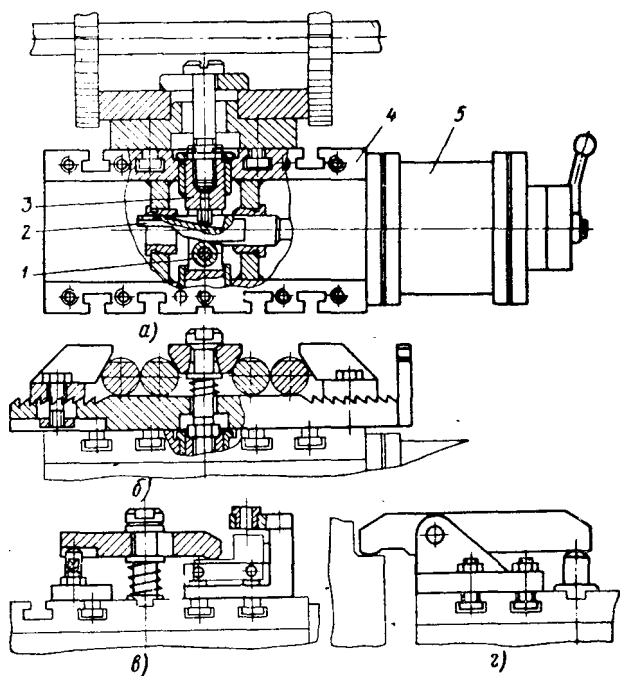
Универсальный силовой гидравлический привод к сверлильным и фрезерным станкам
